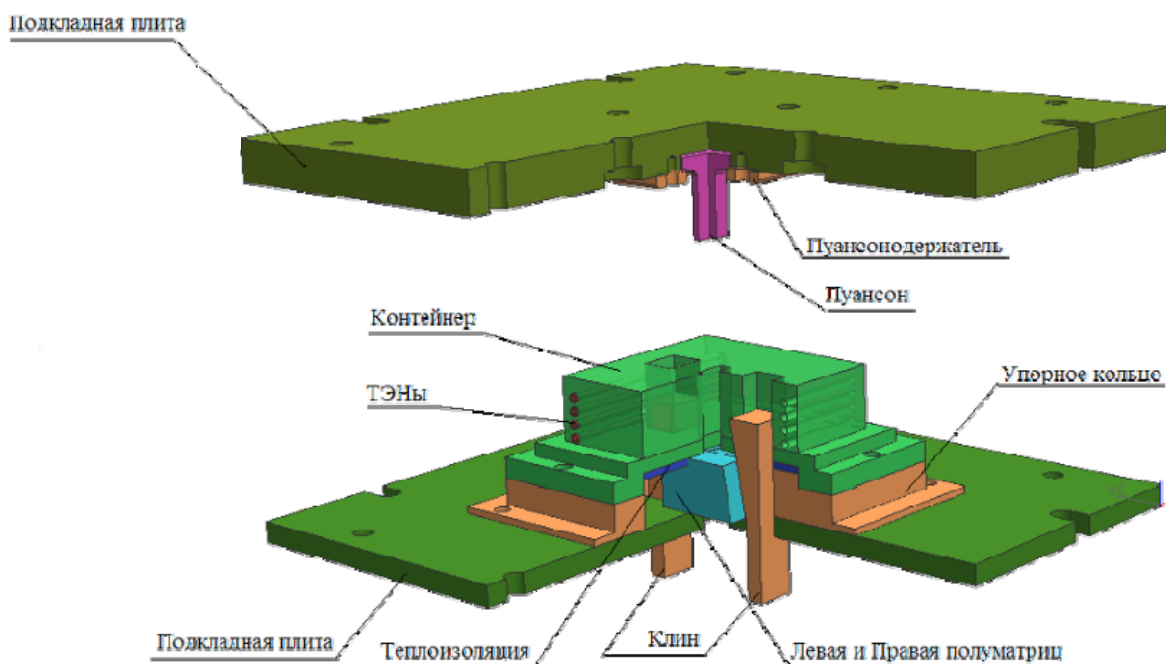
Предлагаемая конструкция установки для выдавливания переменного сечения заготовок лопаток
